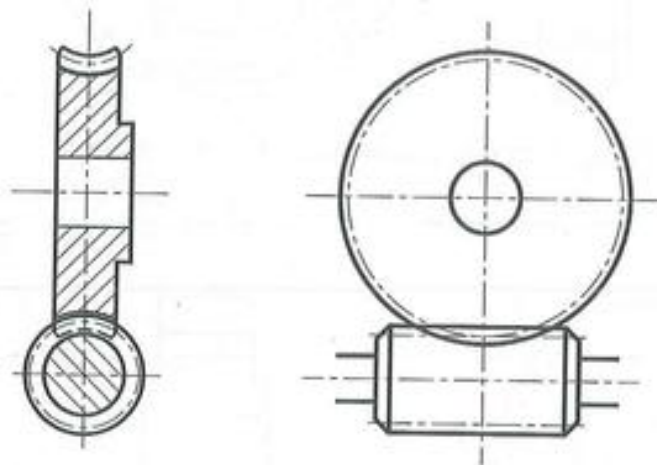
Engranaje de corona con tornillo sin fin.
